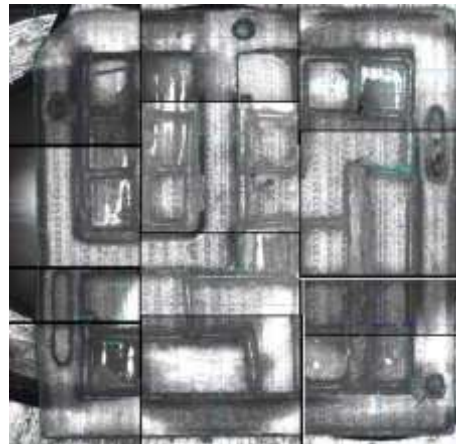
Ensamblaje en molde 4 piso 2, equipo Zoller
